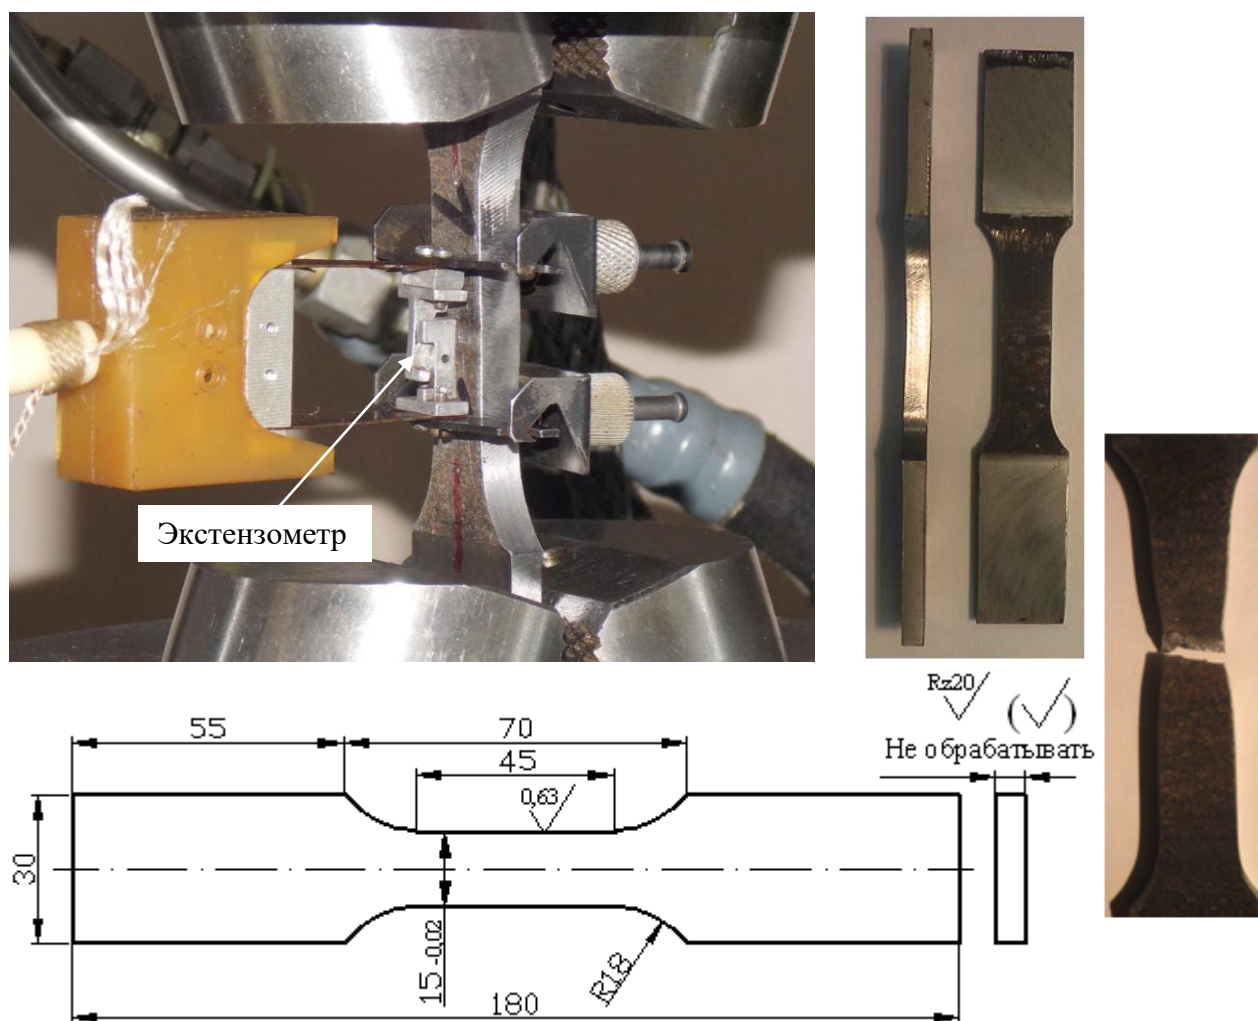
Образец на растяжение, установка образца в стенд и разрушенный образец, (фото приведено для кольцевого образца с недеформированной рабочей частью).
